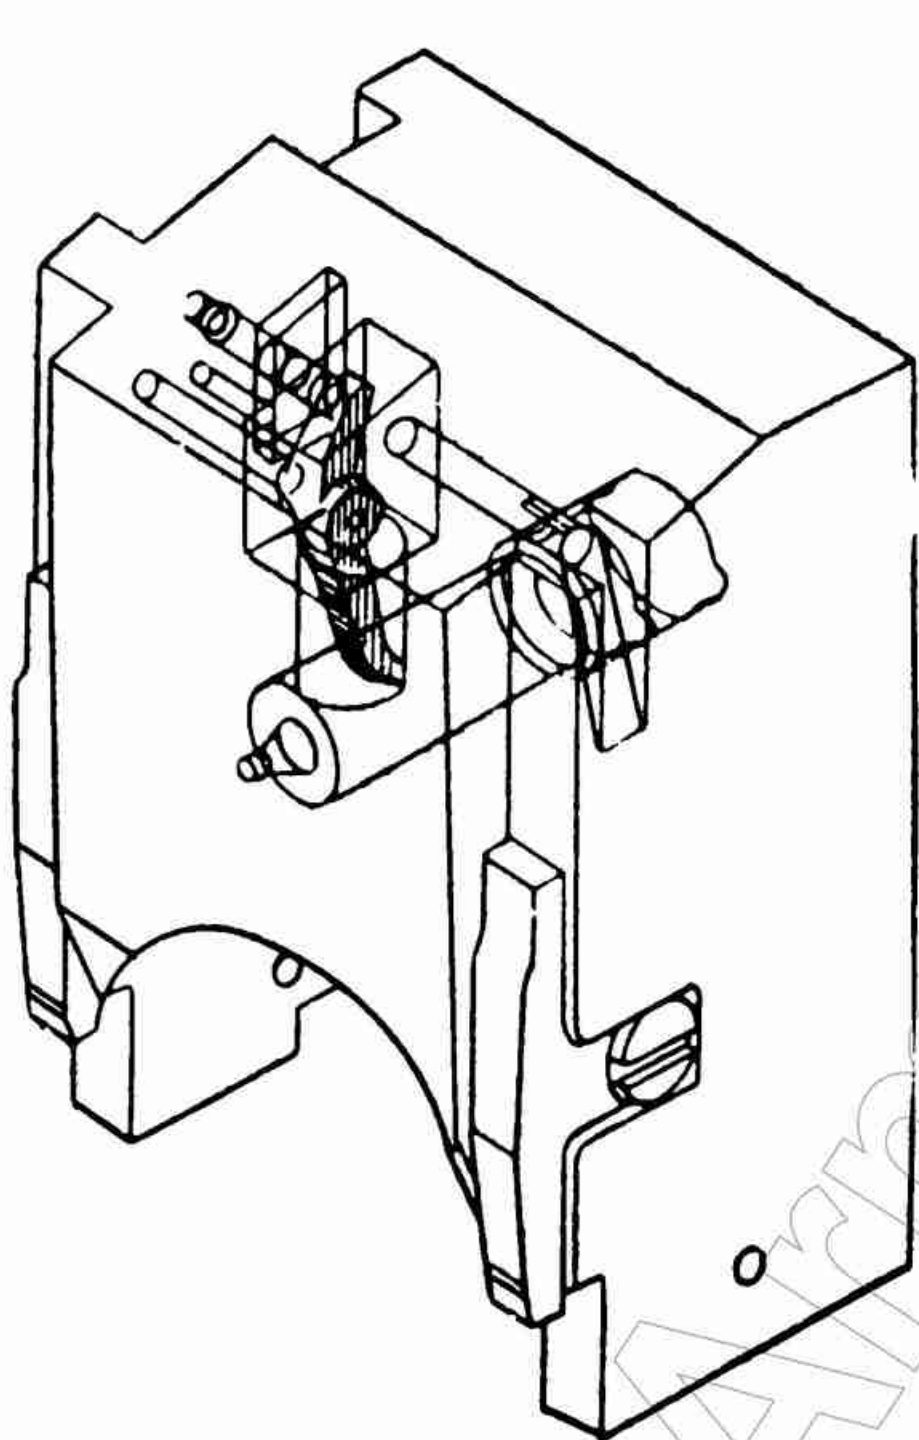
Положение деталей ударного и предохранительного механизмов при сборке
